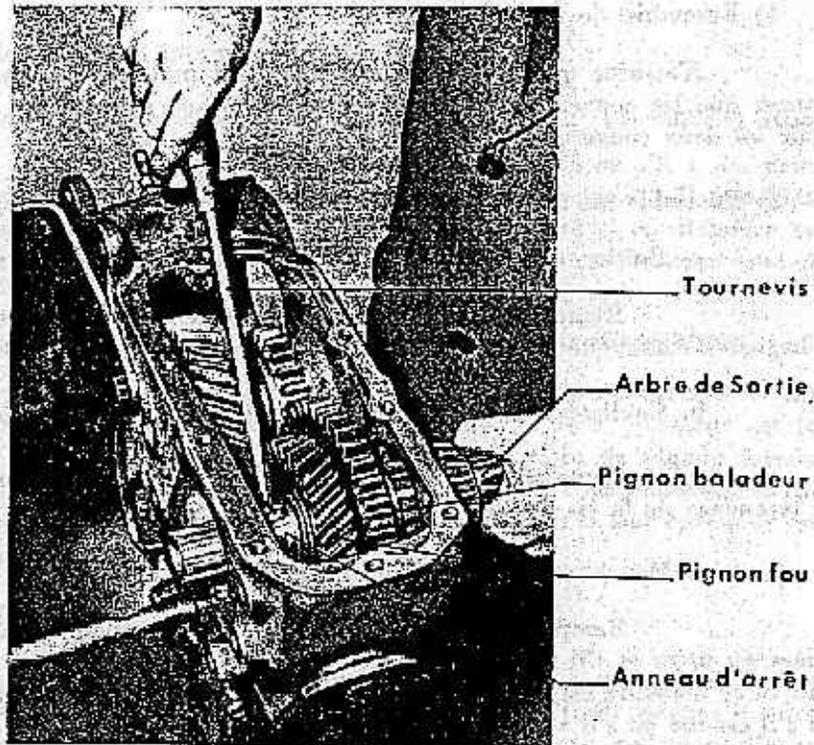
Dégager l'anneau d'arrêt de l'arbre de sortie. Vue de dessous.
